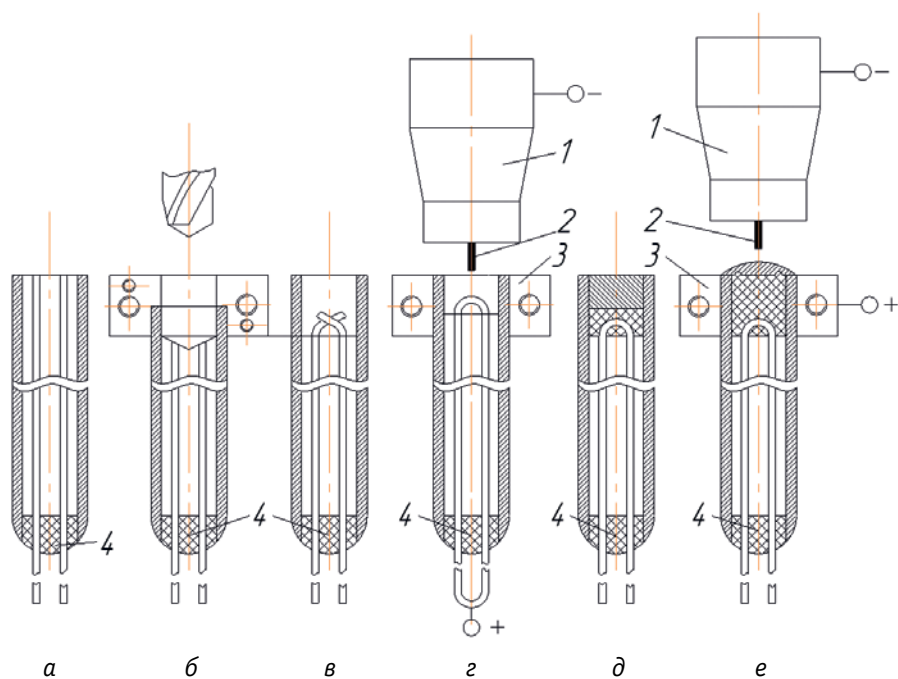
Последовательность подготовки и сварки рабочих концов термопар диаметром 1–6 мм с рабочим спаем, изолированным от оболочки: а – обрезка заготовки; б – удаление изоляции и термоэлектродов; в – подготовка термоэлектродов под сварку; г – сварка термоэлектродов; д – уплотнение изоляции над термоэлектродами и установка пробки; е – сварка оболочки (1 – горелка; 2 – электрод; 3 – медные губки; 4 – герметик)
